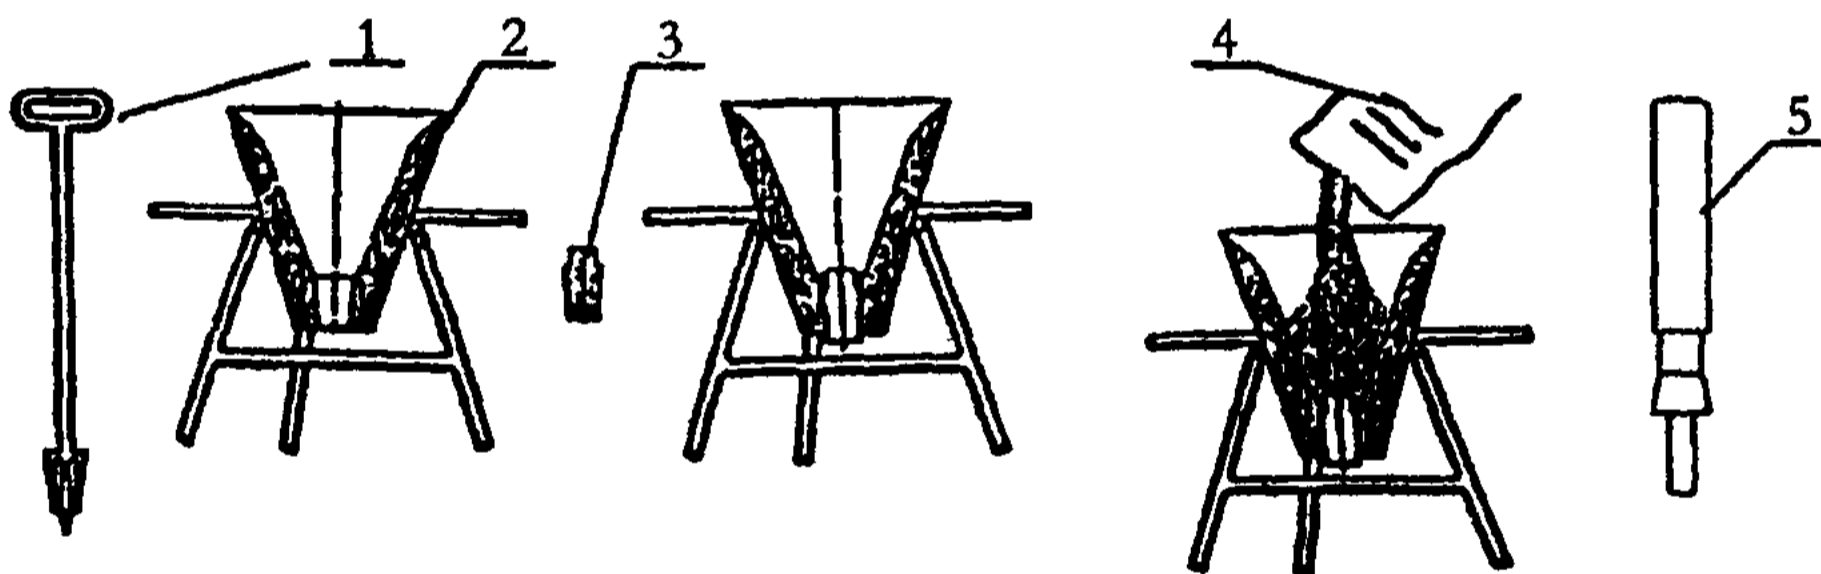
Схема подготовки тигля для алюмотермитной сварки
